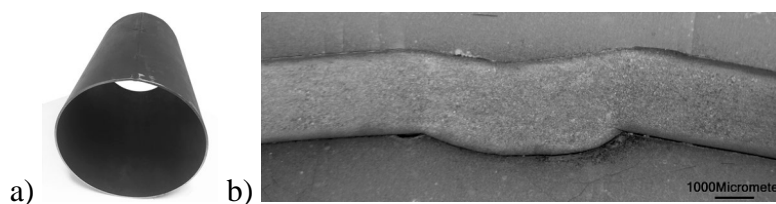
a) Sector de tubo soldado (J-T) y b) Macrografía.
